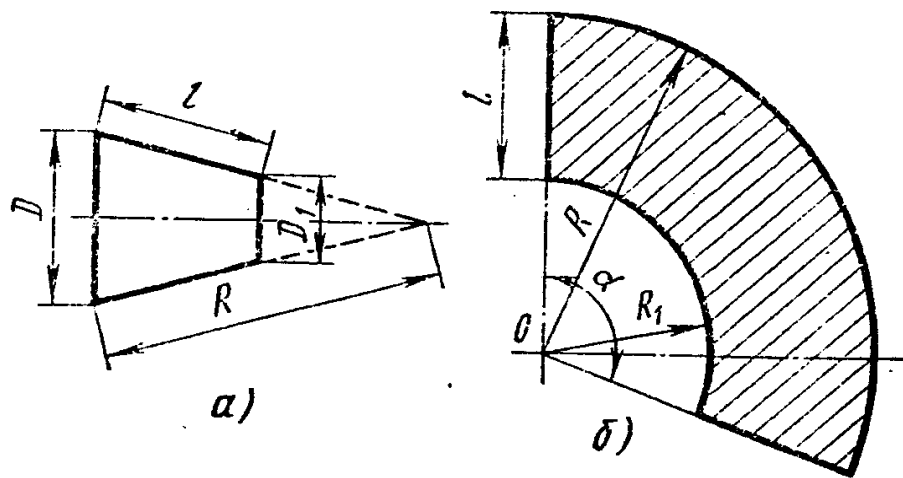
Построение развертки сварного концентрического перехода:
